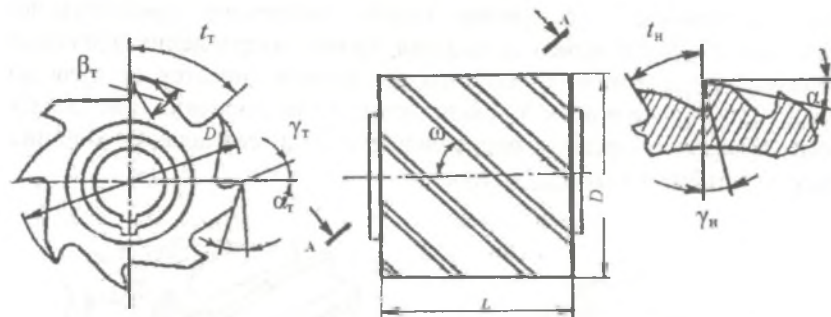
Геометрические и конструктивные параметры цилиндрической фрезы
